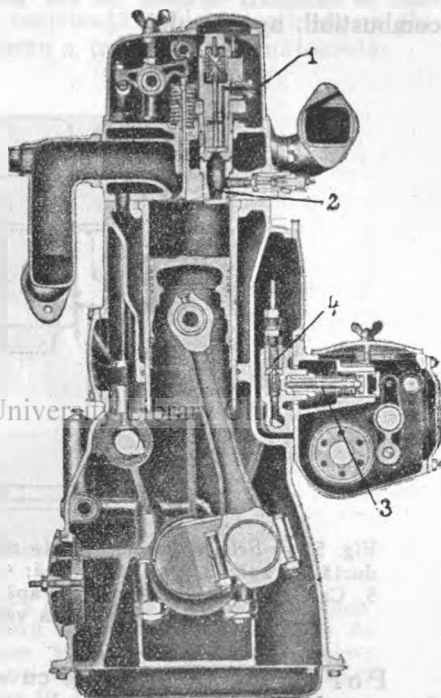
Secțiune prin motor: 1. Teava de combustibil ce vine dela pompa de combustibil spre a intra în ventilul de injecție; 2. Camera de precombustiune; 3 și 4. Pompa de combustibil cu pistonul de pompă acționat (3) de axa cu came și conducte de combustibil spre ventilul de injecție (4).
